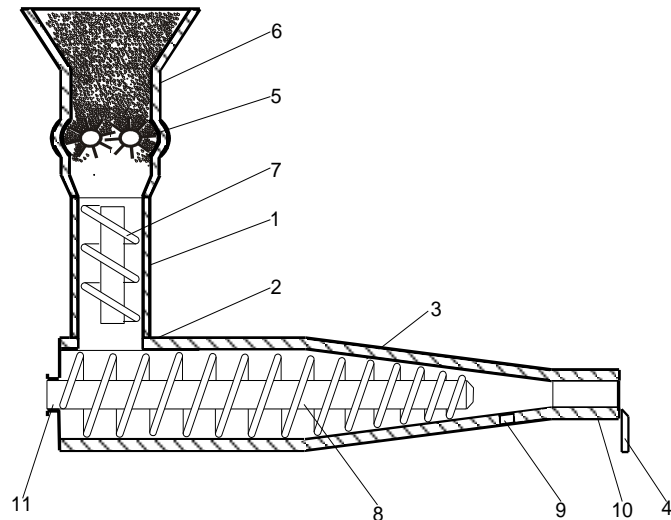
Схема установки для формування паливних матеріалів: 1 – завантажувальний бункер; 2 – циліндрична частина корпусу; 3 – конічна частина корпусу; 4 – ріжучий пристрій; 5 – дозуючий пристрій; 6 – підготовча камера; 7 – дозуючий шнек; 8 – шнек із транспортуючими, ущільнюючими та витискаючими лопатками; 9 – дренажний отвір; 10 – фільтр; 11 – вал редуктора
